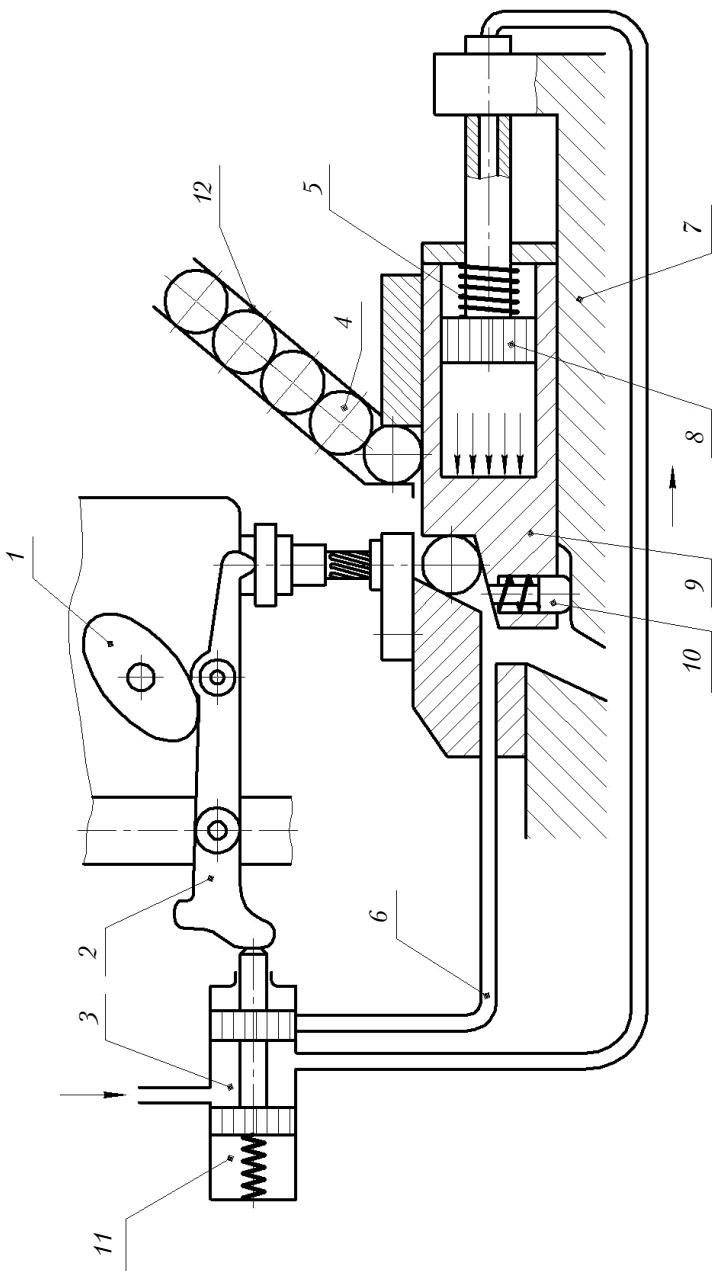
Схема автоматизированного сверлильного приспособления
